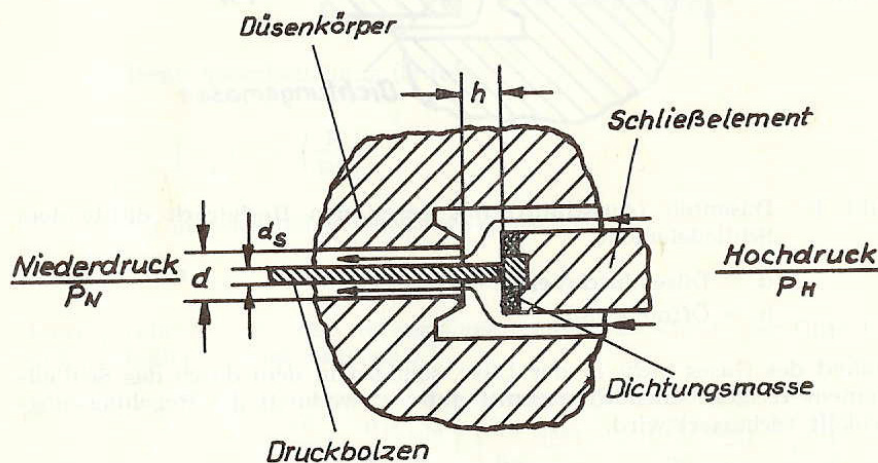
Düsenteil (Ausschnitt) mit Schließelement, das mit dem Hochdruck dichtet
